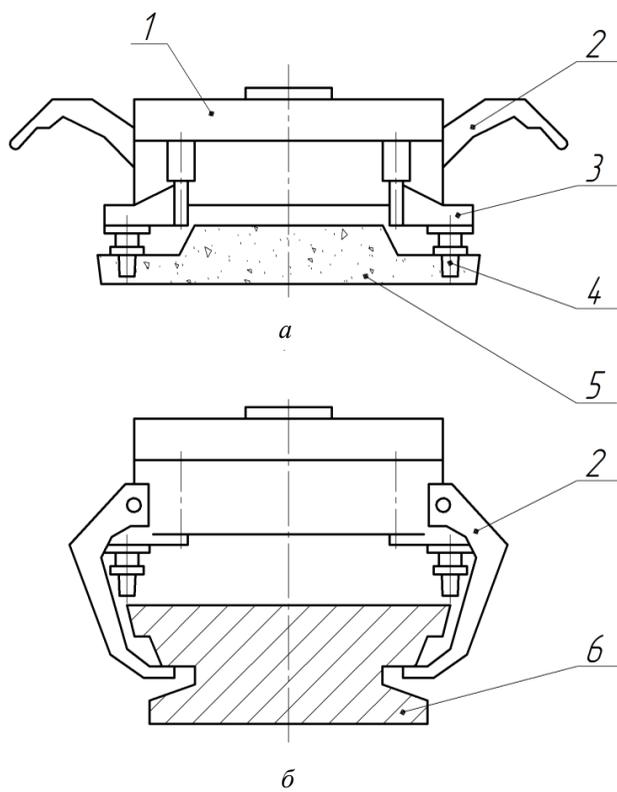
Многофункциональное захватное устройство: *а* – захват стержня; *б* – схема захватывания отливки; *1* – фланец; *2* – пальцы-рычаги; *3* – кронштейны; *4* – эластичные надувные фиксаторы; *5* – стержень; *б* – отливка
